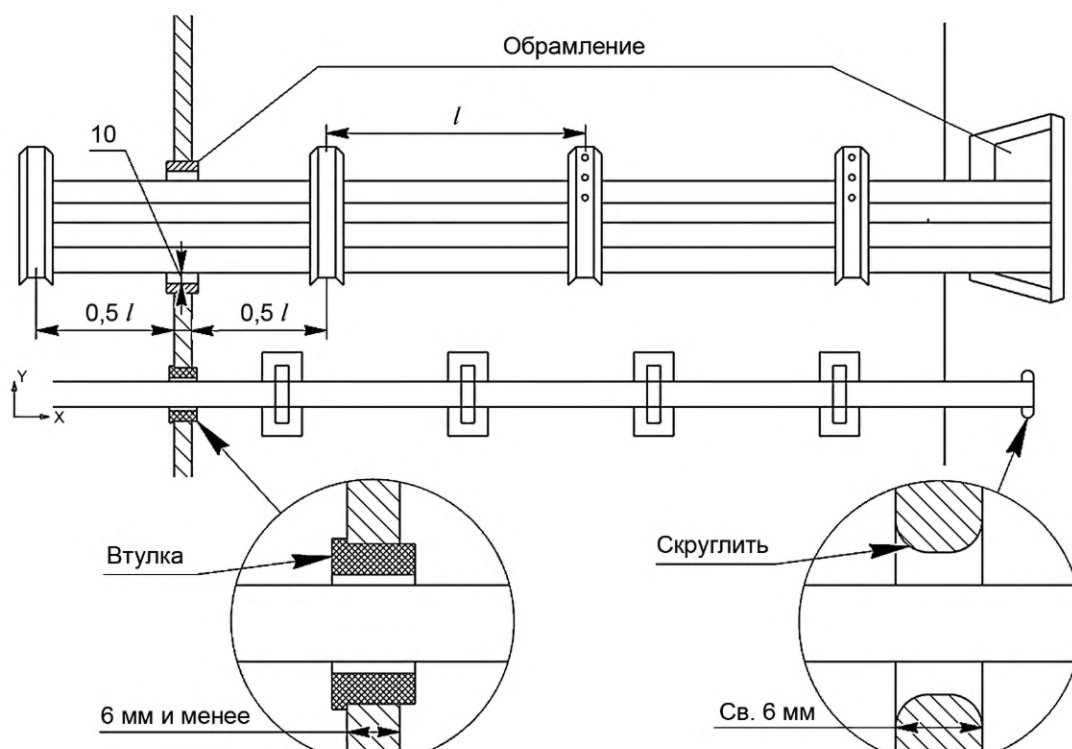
Проход кабелей через пронцаемые переборки или набор корпуса
